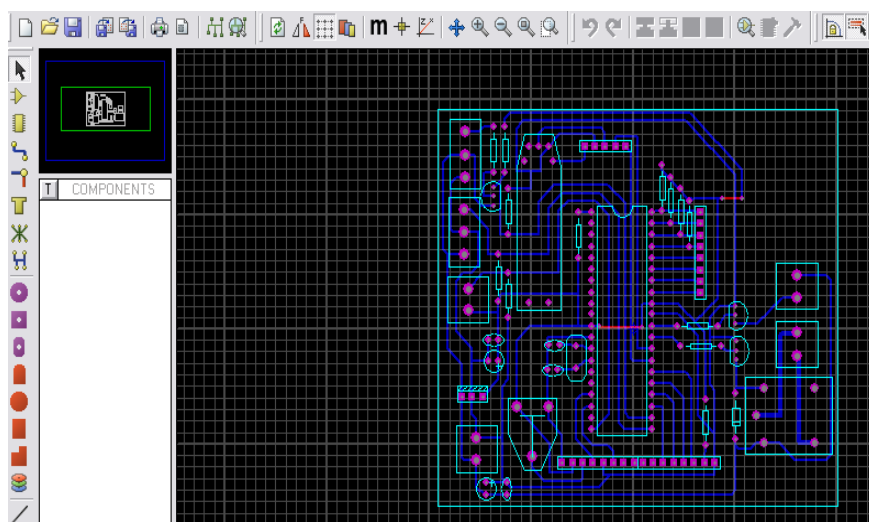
A DISEÑO PCB PROGRAMA PROTEUS
